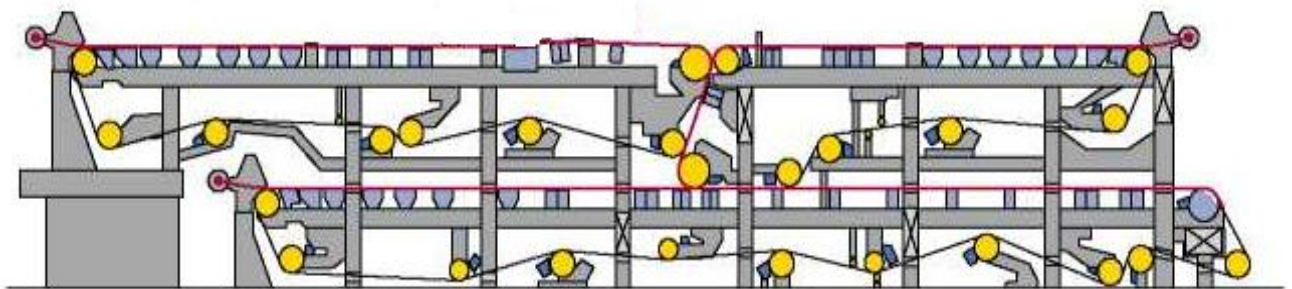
3- Плоскосітковий формувальний пристрій
